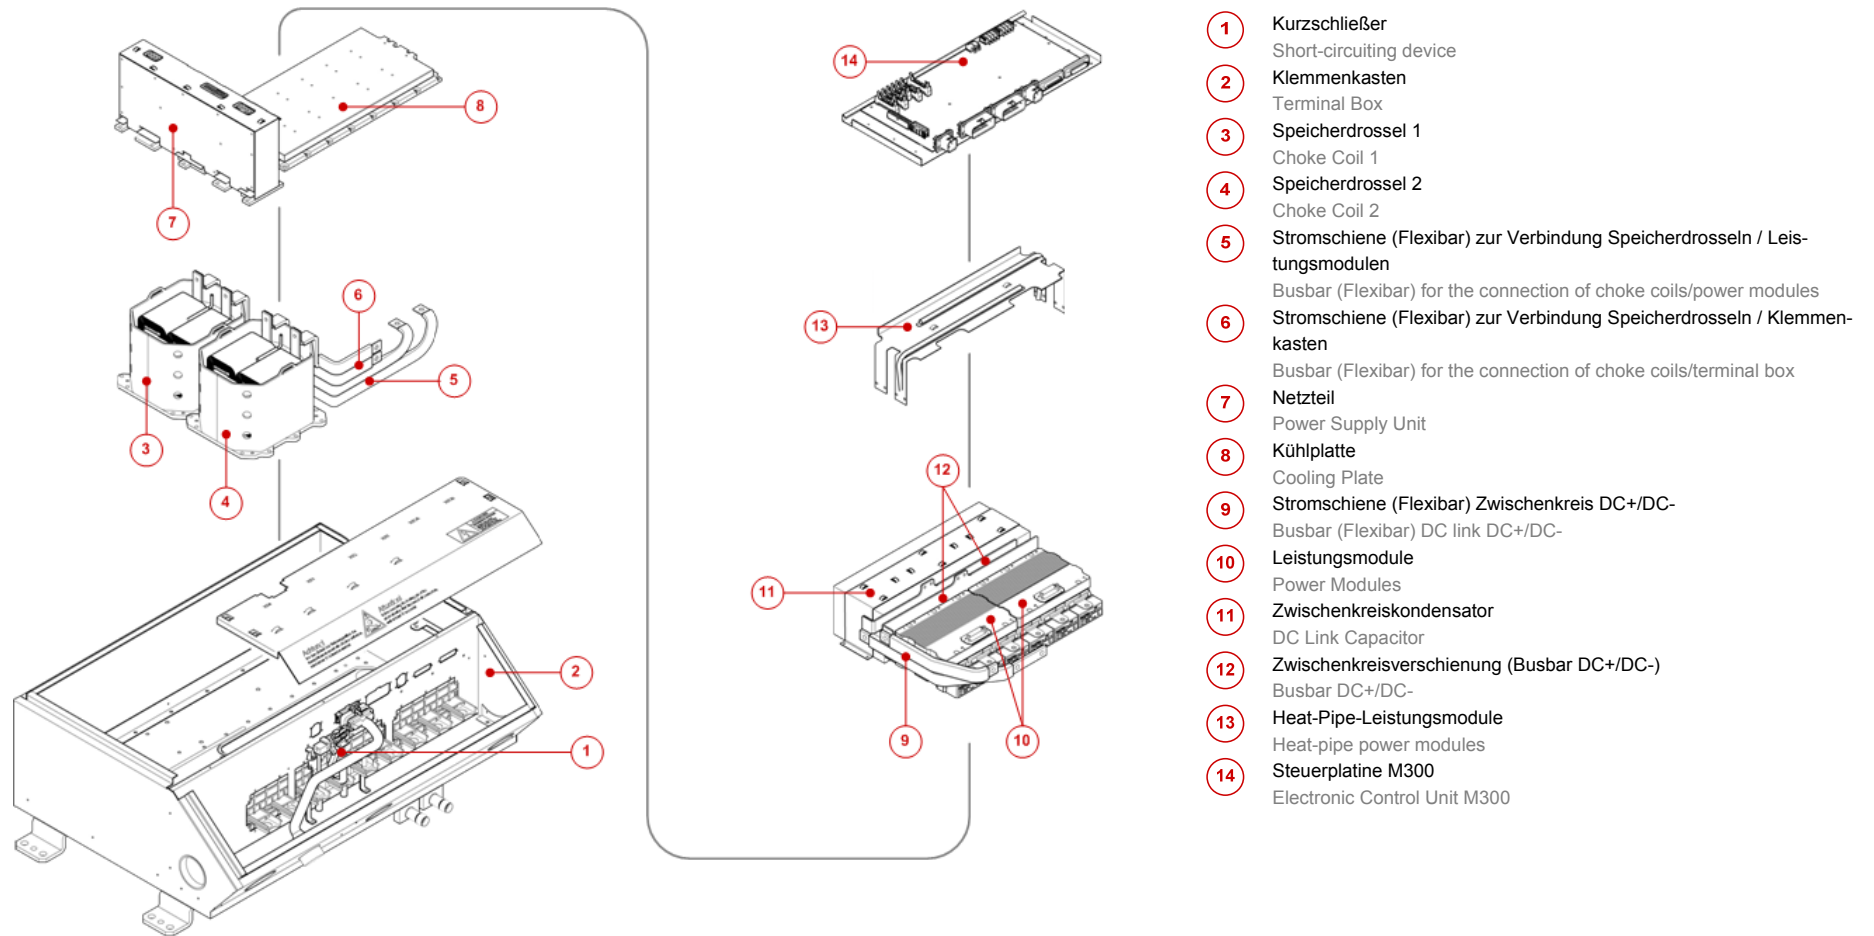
Explosionszeichnung VHC-Komponenten / Exploded view VHC-components
